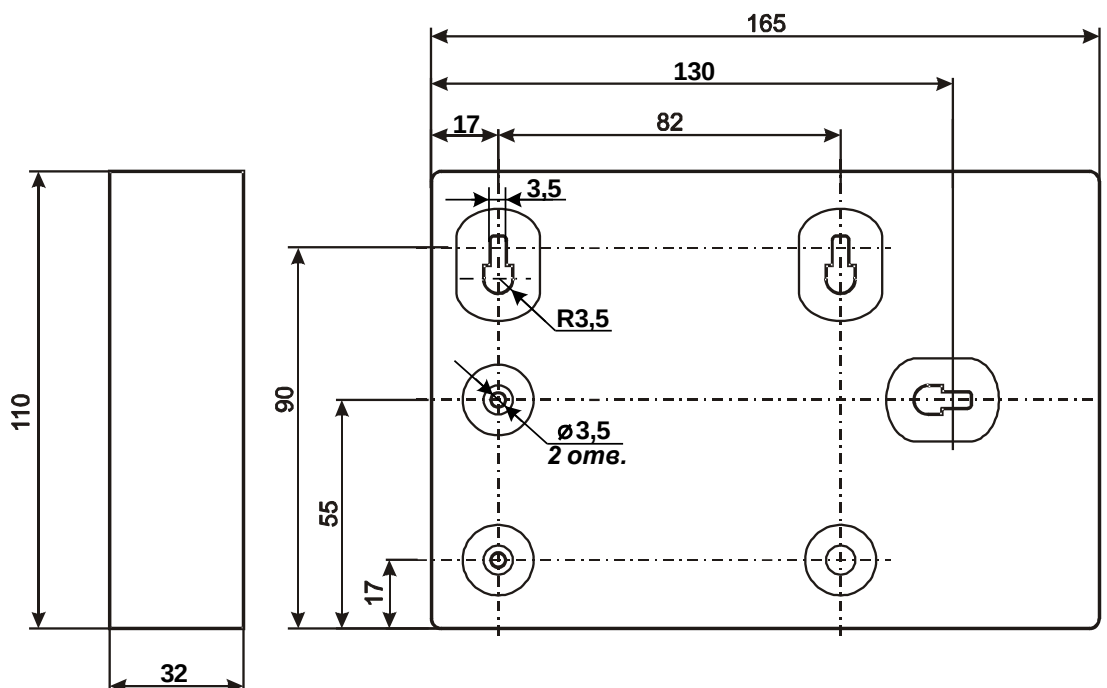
Габаритные и присоединительные размеры корпуса ТИ
